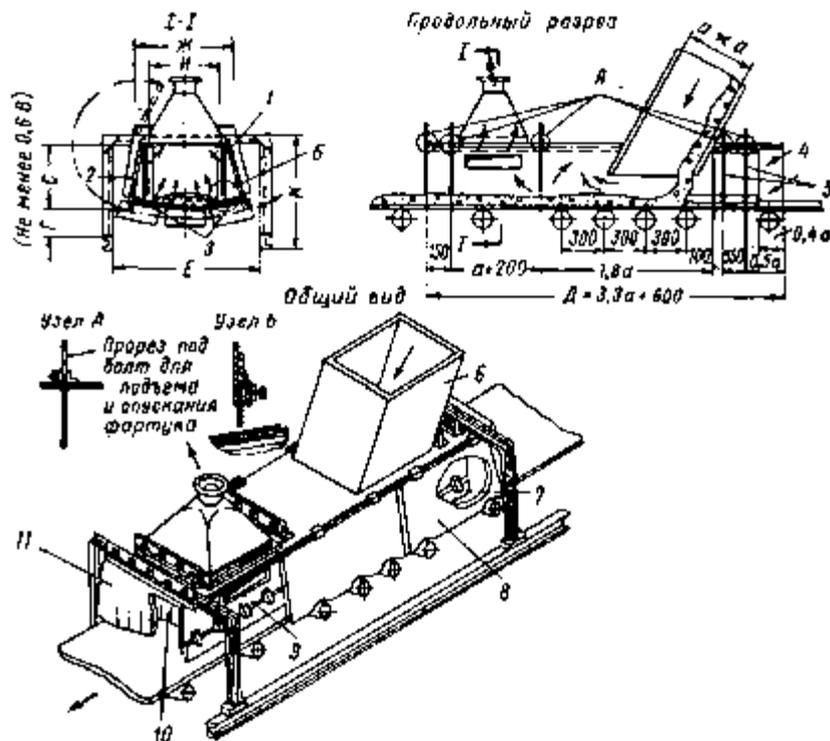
Укрытие с боковыми вентиляционными камерами конструкции СИОТ:
